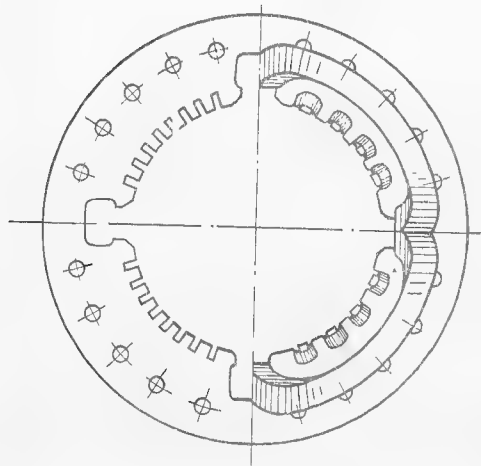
Обмотка возбуждения машины индукторного типа
